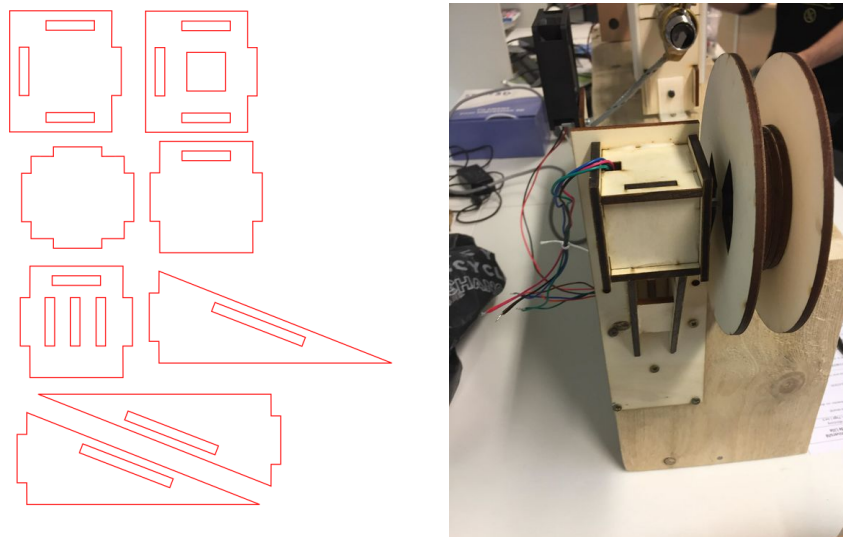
Assemblage et montage sur la boîte du système d'enroulement
